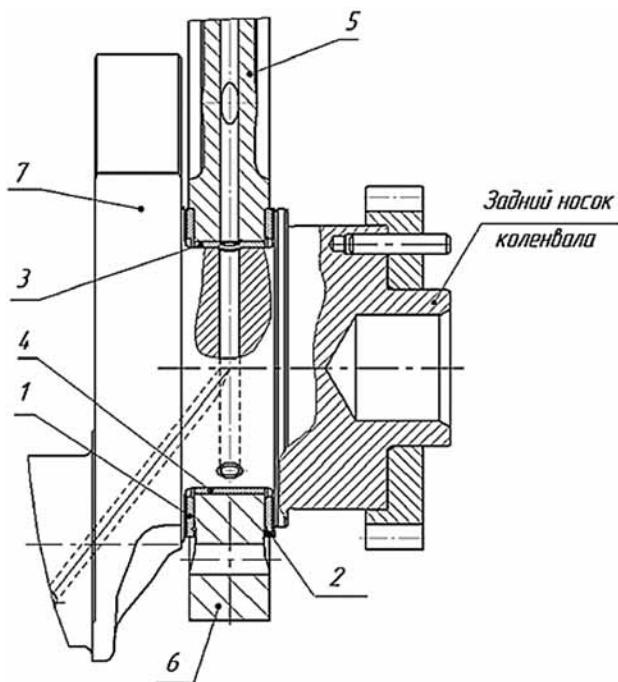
Установка осевых подшипников коленчатых валов двигателей ПАО КамАЗ:
